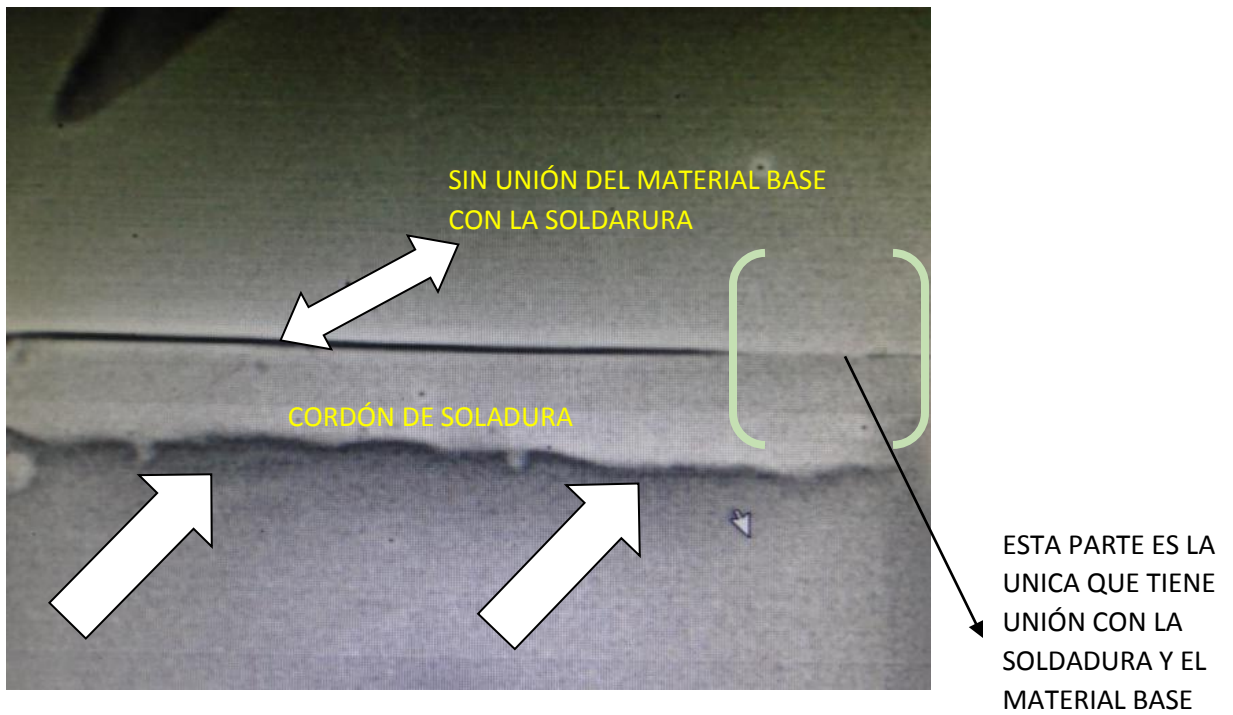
Cordón de soldadura. (Rechazado)
